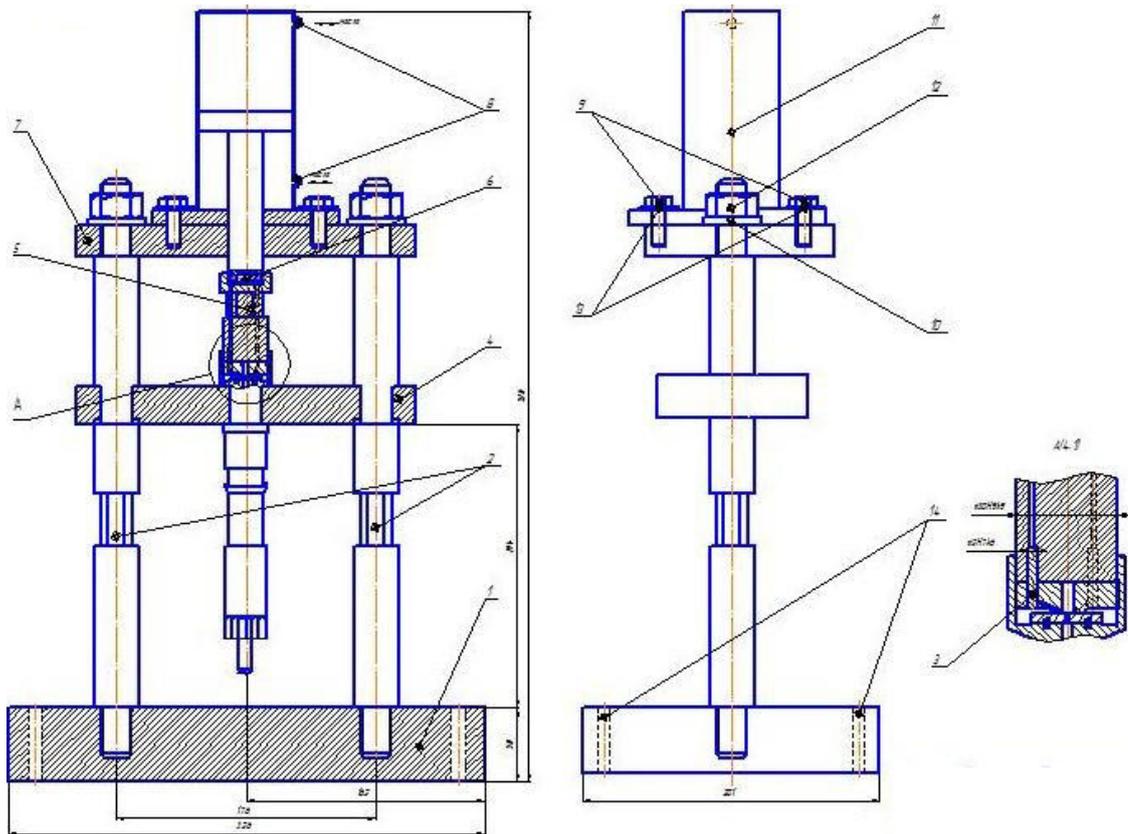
Чертеж разработанного устройства для разборки-сборки форсунок: 1-нижняя плита; 2 – болт; 3 – форсунка; 4 – средняя плита; 5 – ключ; 6 - подшипник; 7 – верхняя плита; 8 – штуцеры; 9 – болт М8; 10 – шайба М20; 11 – гидроцилиндр; 12- гайка М20; 13- шайбы М8; 14 - отверстия для болтов.
